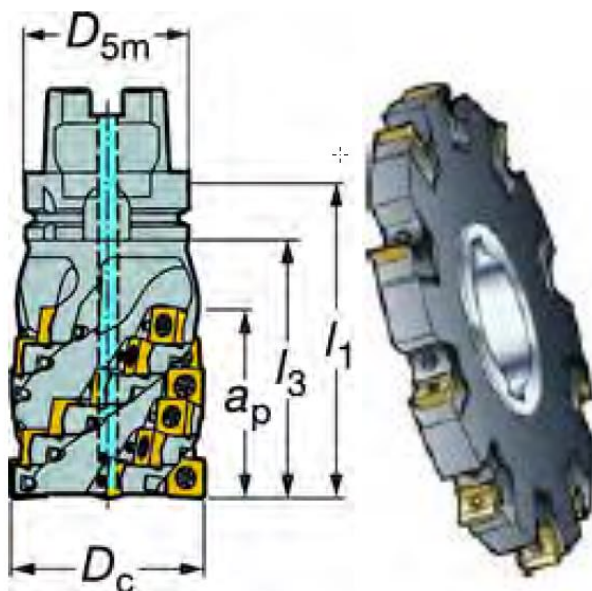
Конструкции длиннокрайной и дисковой пазовой фрез
